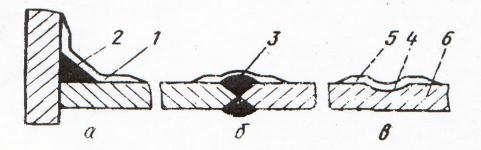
Схема укладки шпонок и полосок на неровности поверхности котла: а - угловой шов; б - сварной шов с выступом; в - вмятина стенка котла; 1 - шпонка; 2, 3 - угловой и стыковой сварные швы; 4 - неровность; 5 - полоски; 6 - стенки котла.
